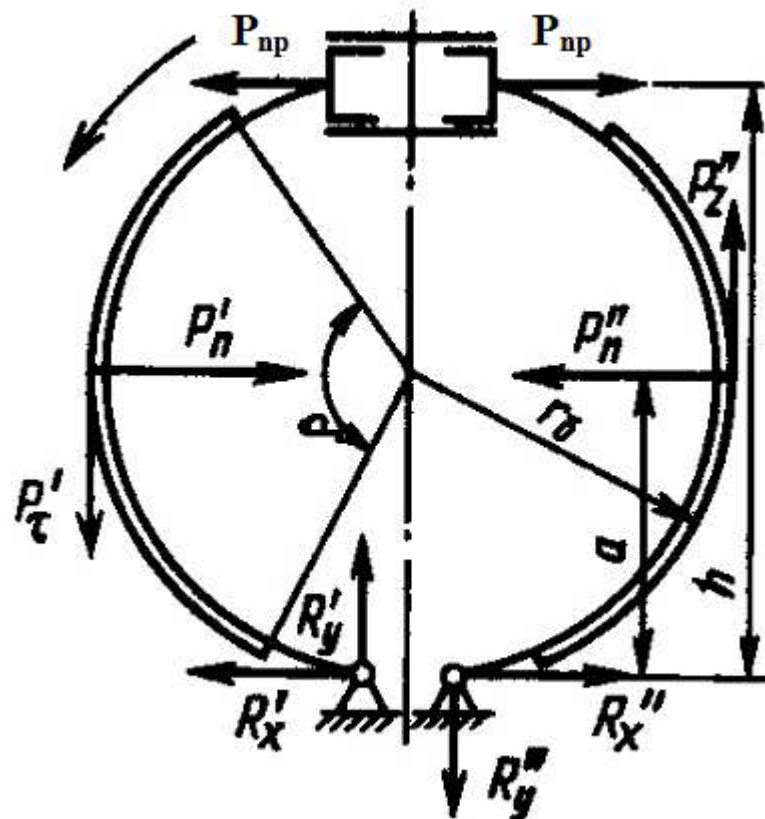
Схема барабанного тормозного механизма с равными приводными силами и односторонним расположением опор
